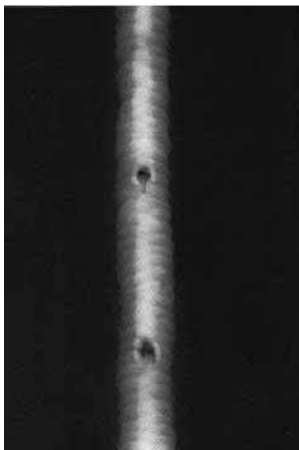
7 *Junta soldada con quemón en la raíz.
